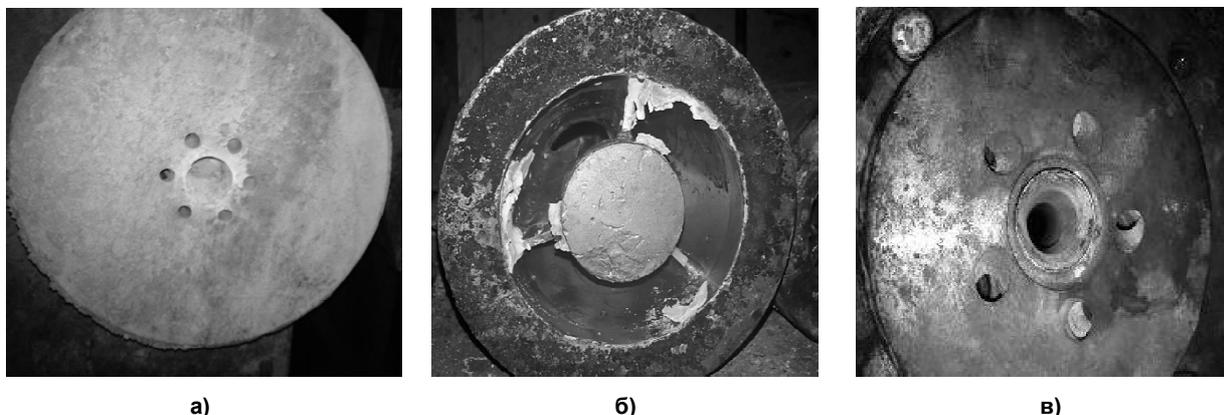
Примеры конструкций форсунок для нанесения СДМ на внутреннюю поверхность нагретой гильзы
